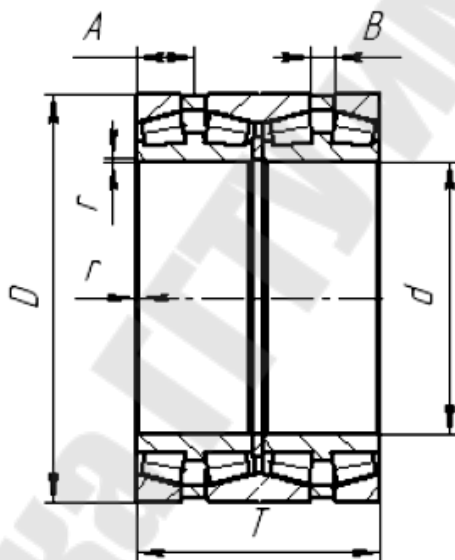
Подшипник роликовый радиально-упорный конический четырехрядный.
